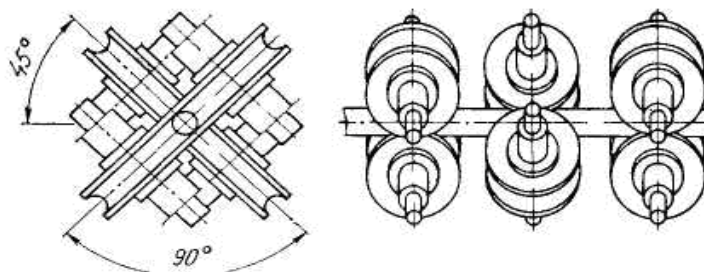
Кинематическая схема клетки калибровочного стана
